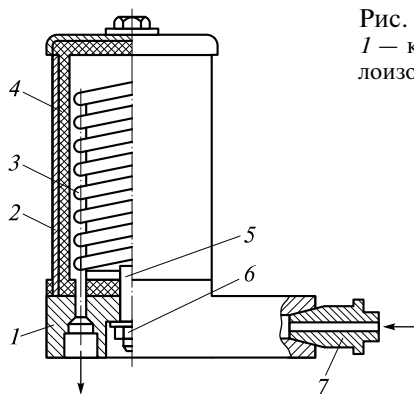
Подогреватель углекислого газа: 1 — корпус; 2 — кожух; 3 — змеевик; 4 — теплоизоляция; 5 — нагревательный элемент; 6 — накидная гайка; 7 — зажим
